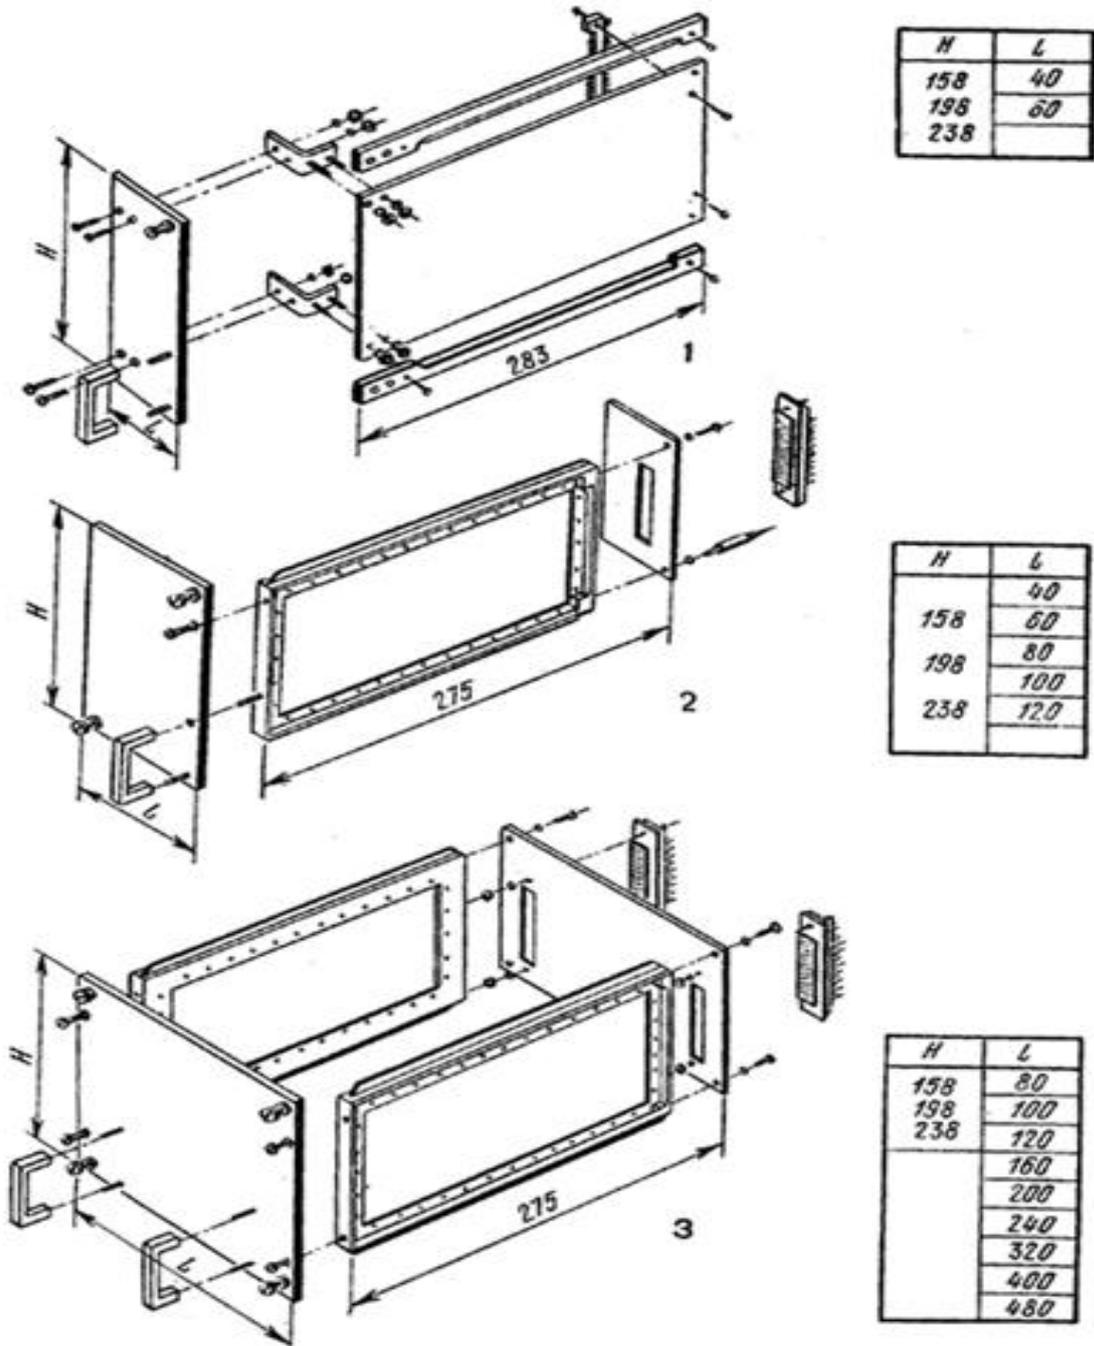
Схема конструкций частичных корпусов комплекса универсальных типовых конструкций УТК РЭС [5]
